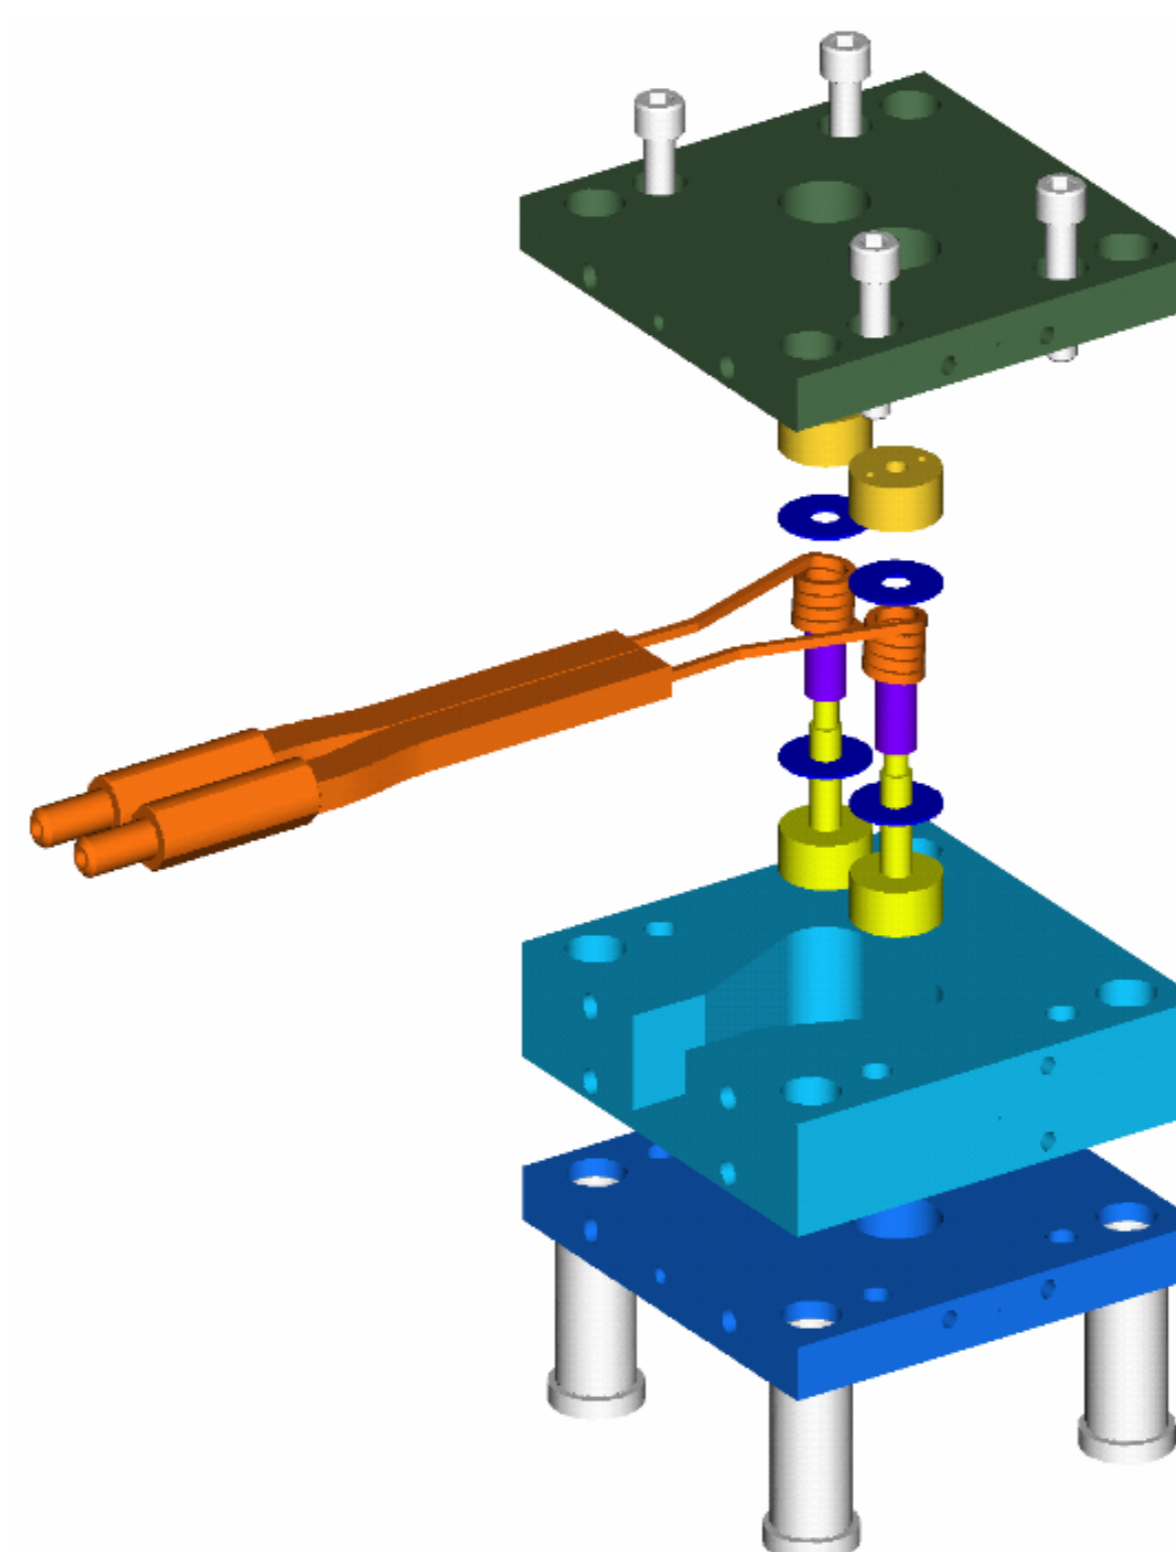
Werkzeug für dünnwandige Hülsen mit vollintegriertem Induktor [2]
